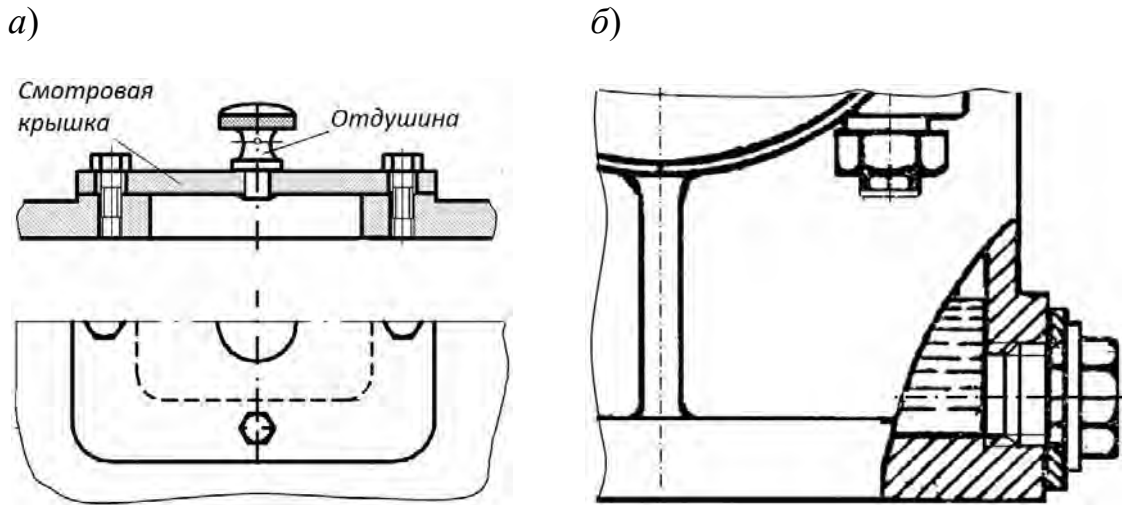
Элементы корпуса редуктора: а – смотровая крышка (люк) с отдушиной (крышка – отдушина); б – сливная пробка
